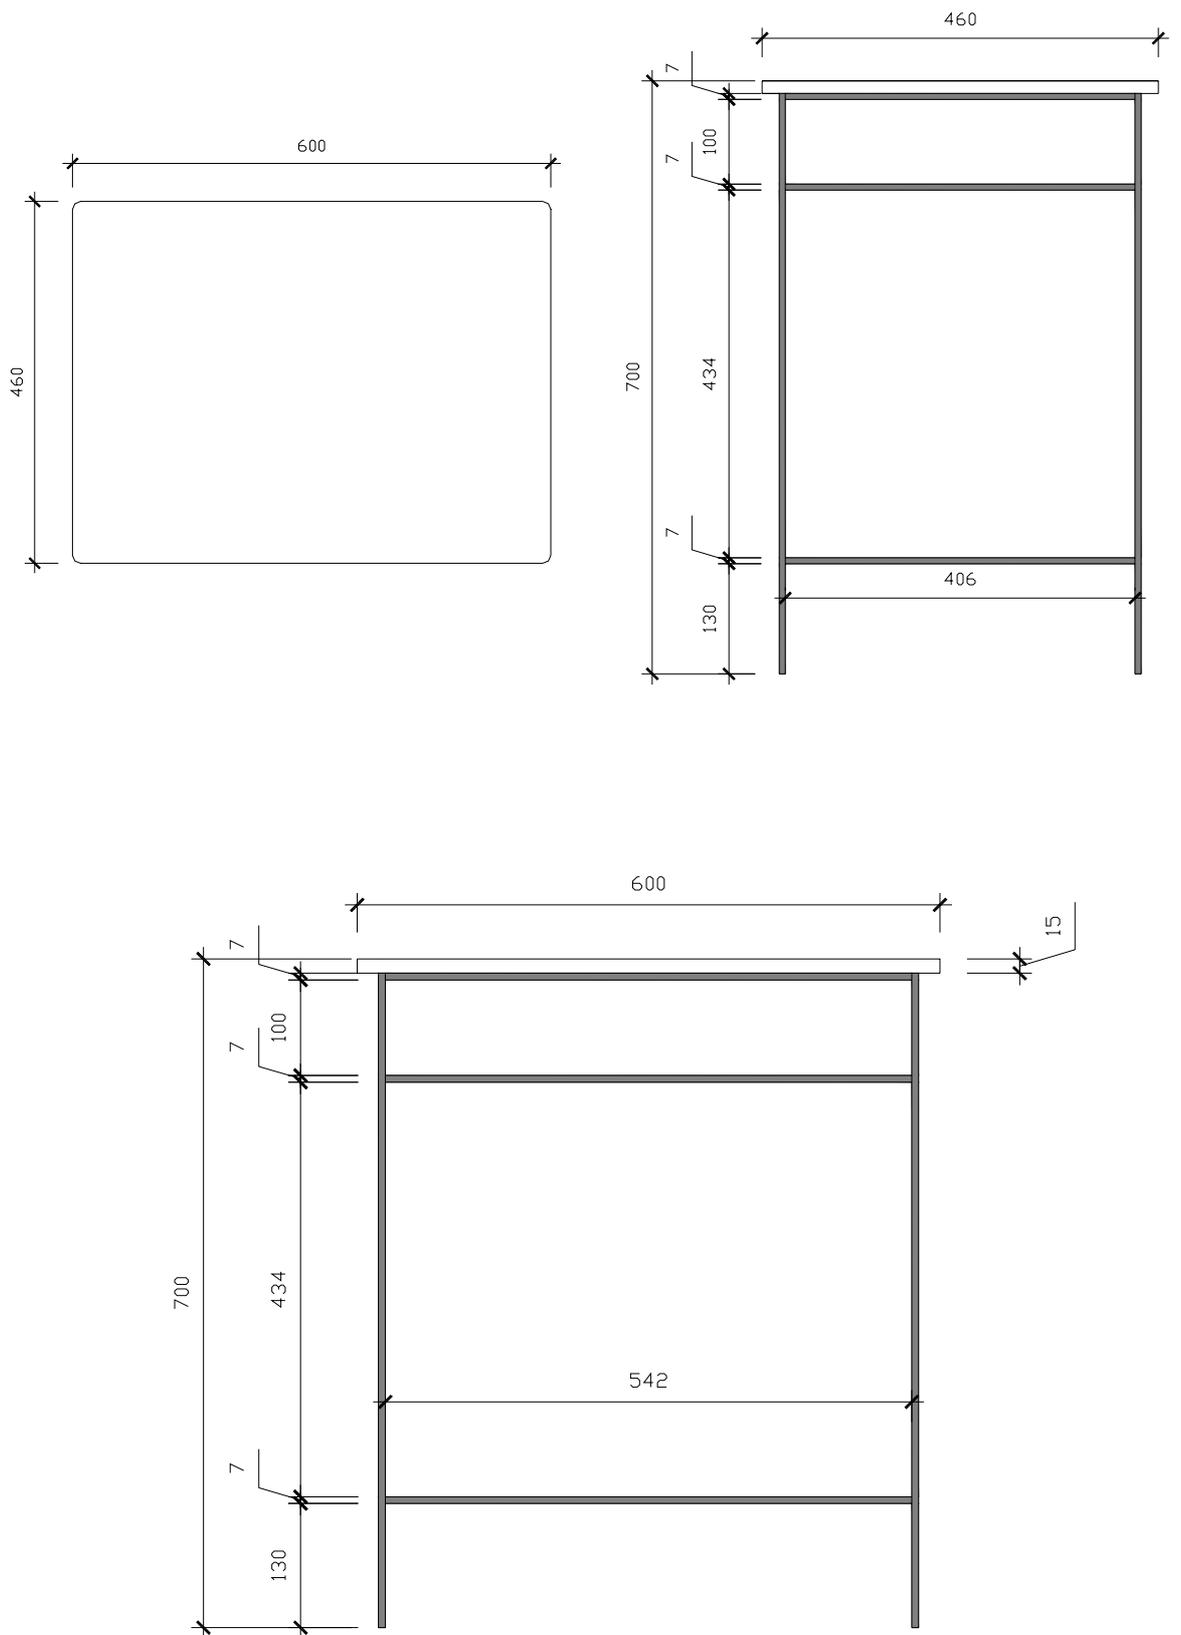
Mesa 3 com vistas superior, lateral e frontal.
